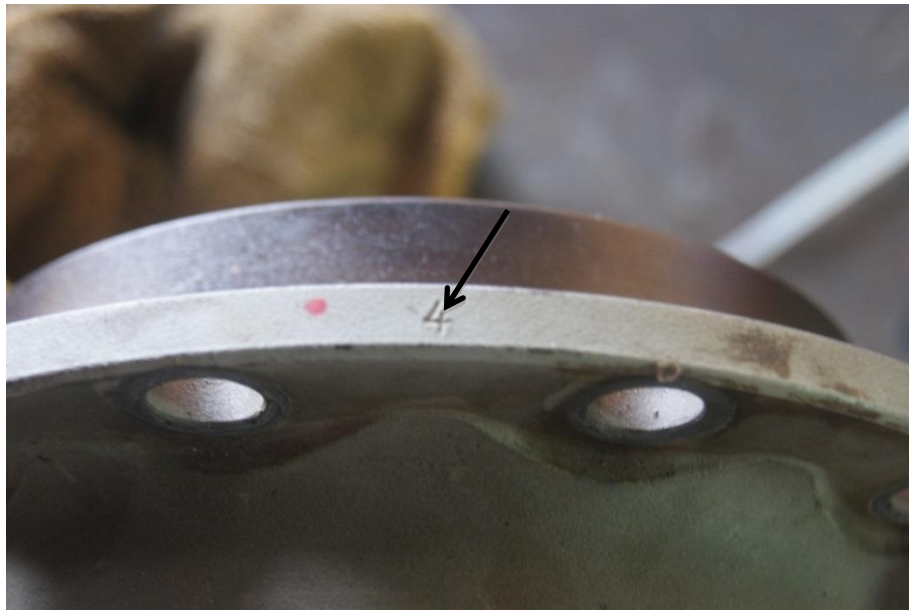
Número posicional del cilindro del motor TC IO 360 D.
